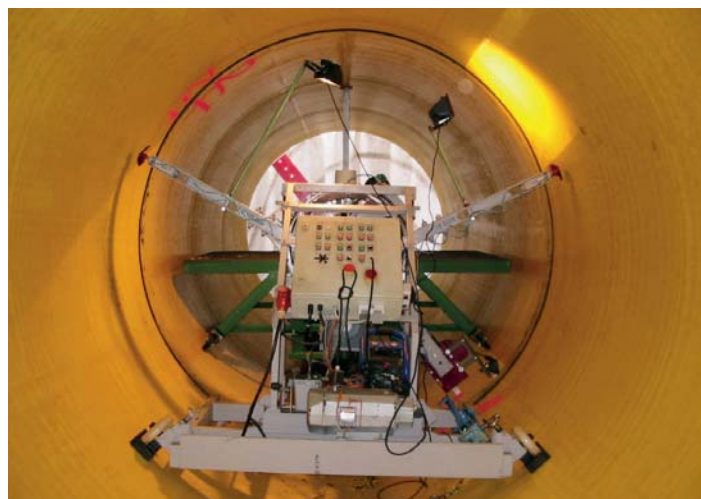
Schweißautomat für Durchmesser bis d 3.000 mm
